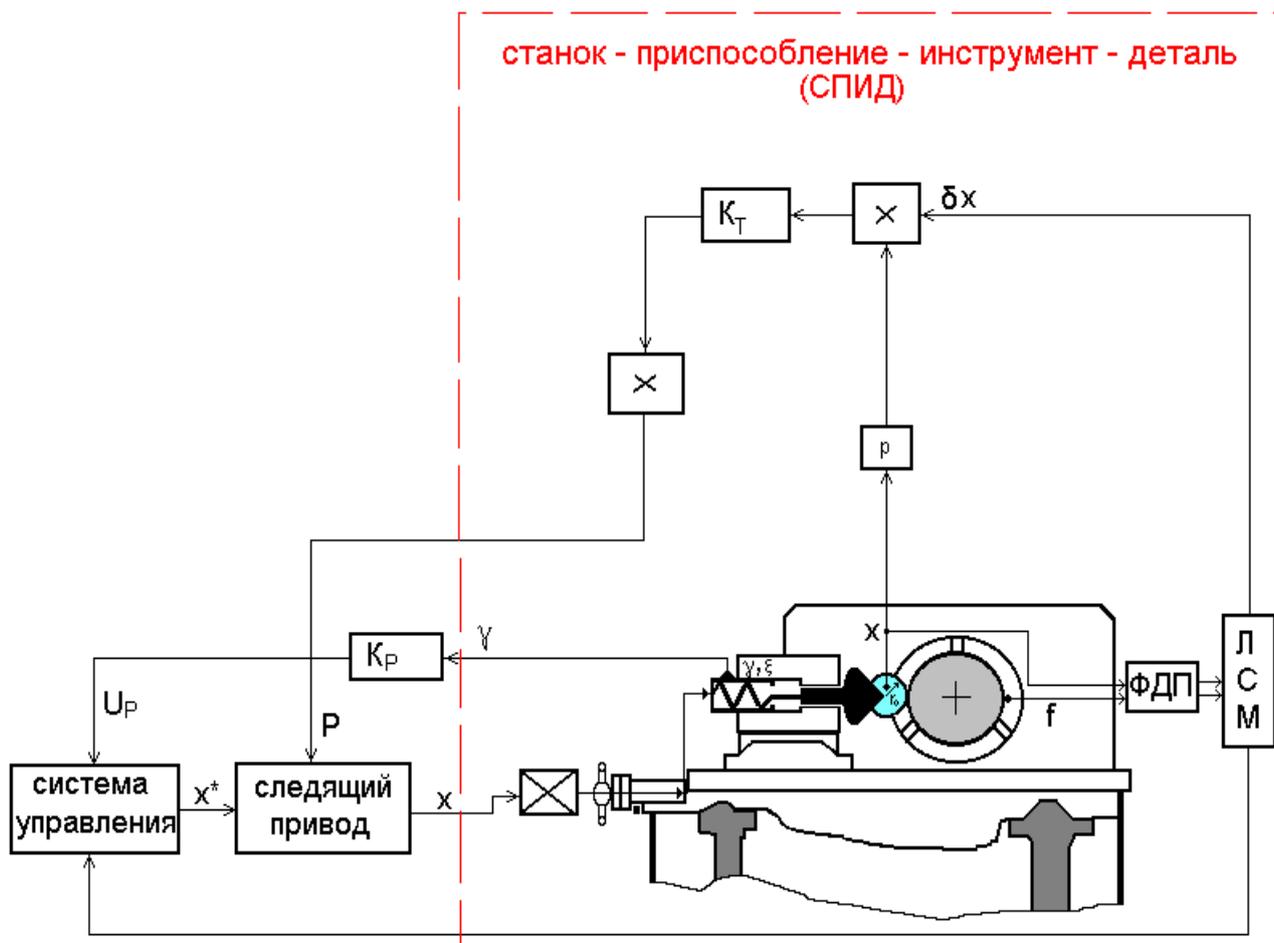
Кинематическая замкнутая схема управления одномерной модели следающего привода для шлифования цилиндрических поверхностей
